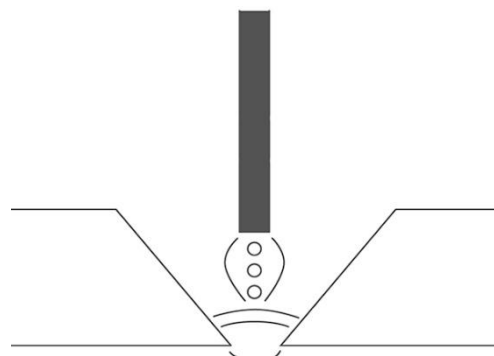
Soldadura eléctrica manual sin soplo magnético ^[6]
